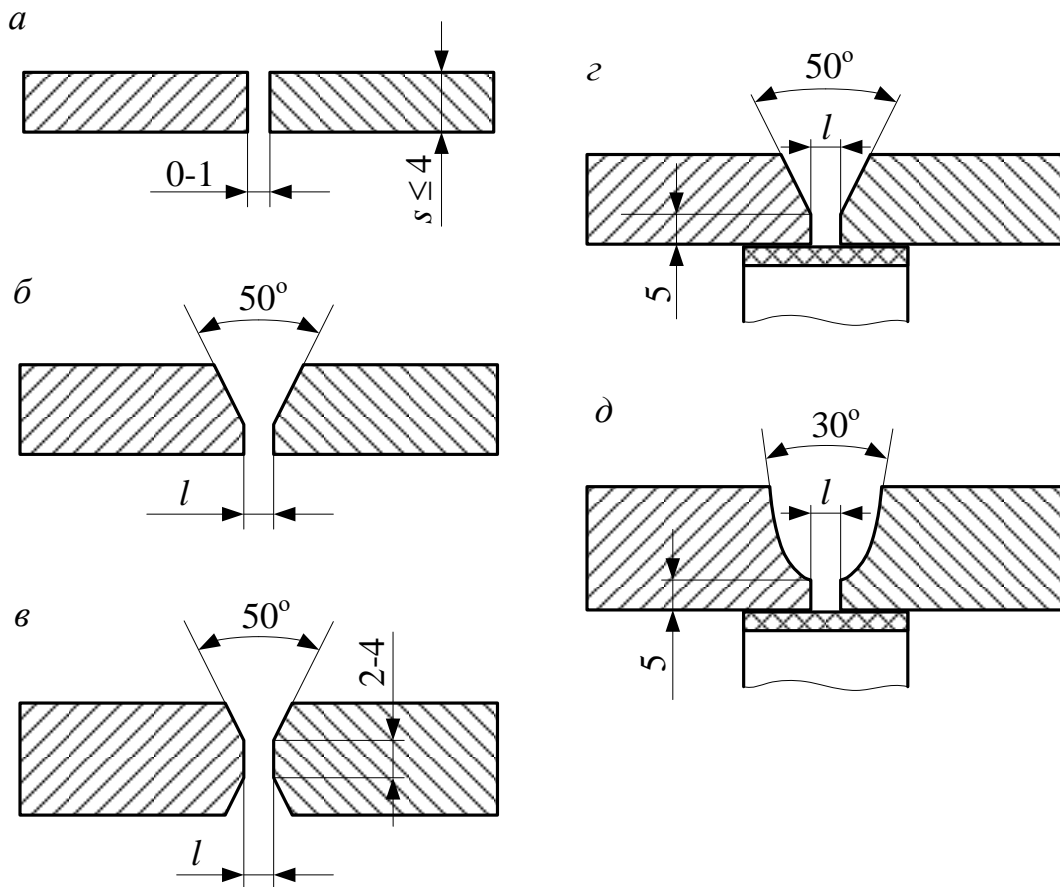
Підготовка кромки для автоматичного зварювання під шаром флюсу:
